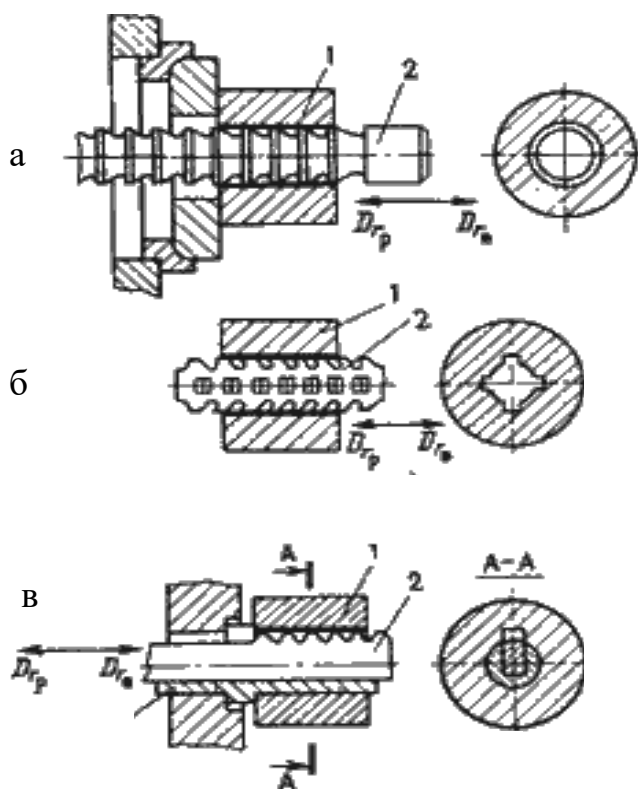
Схемы обработки заготовок на протяжных станках:
